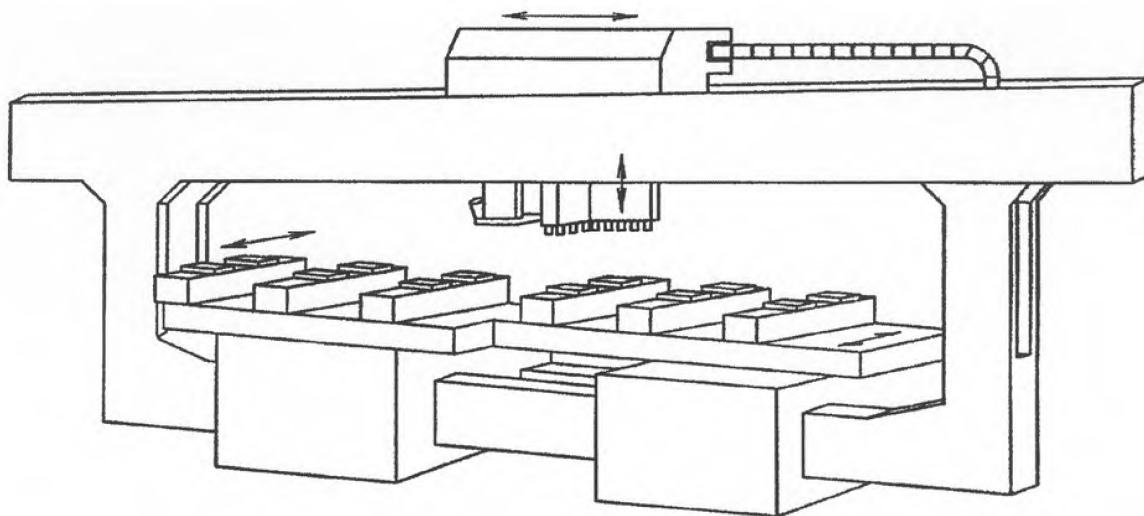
Сверлильный станок портального типа (подвижный стол, неподвижный портал, подвижная головка)¹
